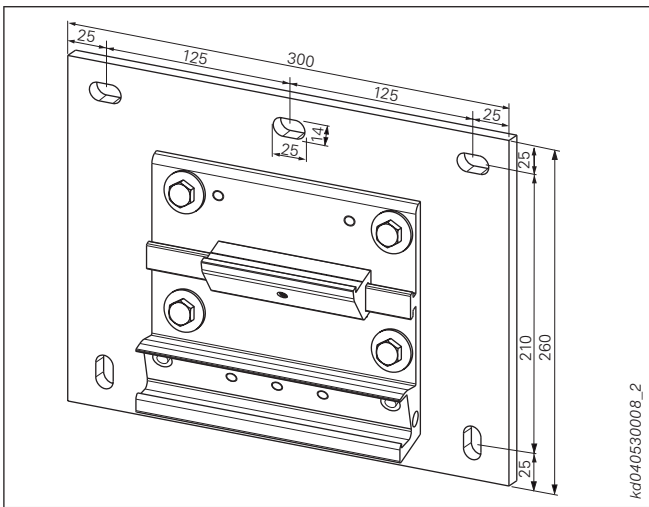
Consola tipo D – Fijación mural con placa de montaje fija
